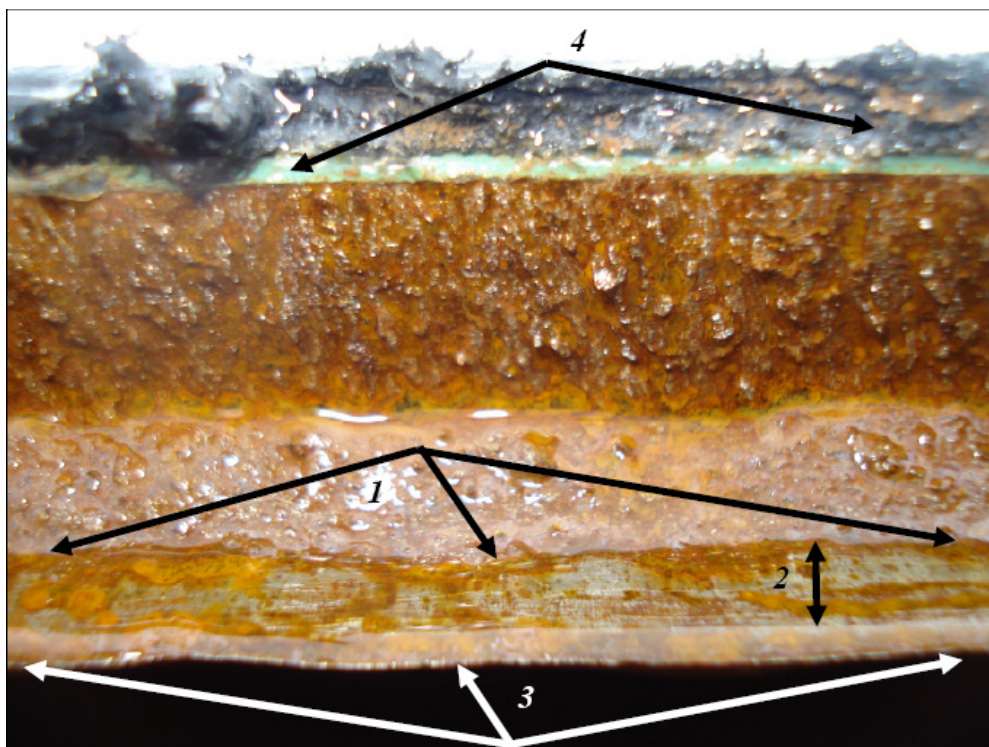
Дефекты сварного соединения в области разрыва трубы
